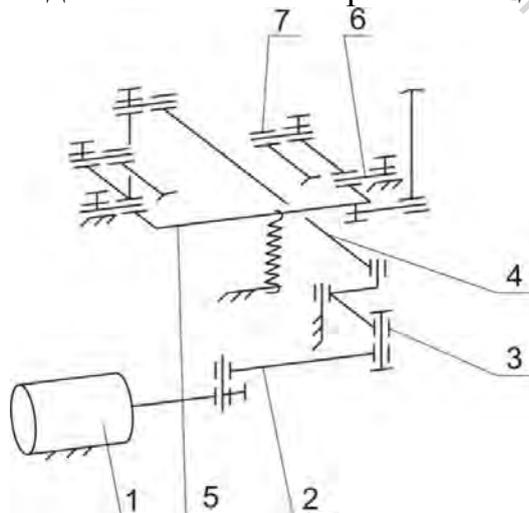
Кинематическая схема узла автоматической закрепки
